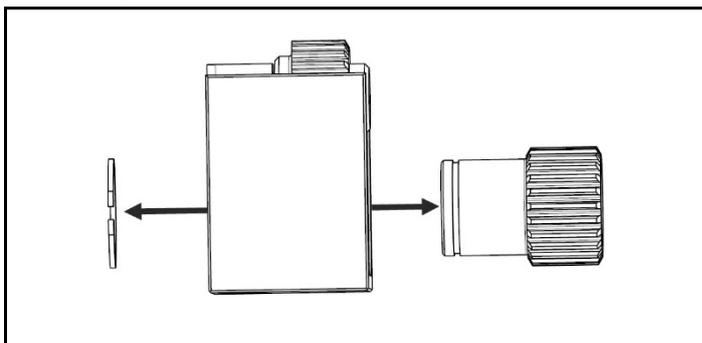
Remova o anel de trava da engrenagem acionadora e a engrenagem acionadora
